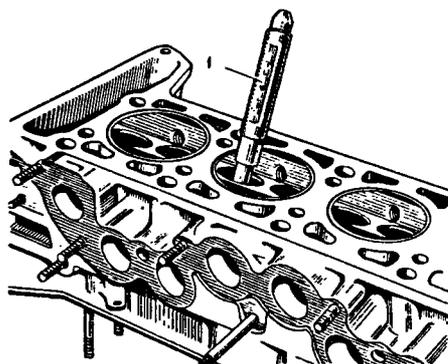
Выпрессовка направляющих втулок: 1 - оправка А.60153/R
